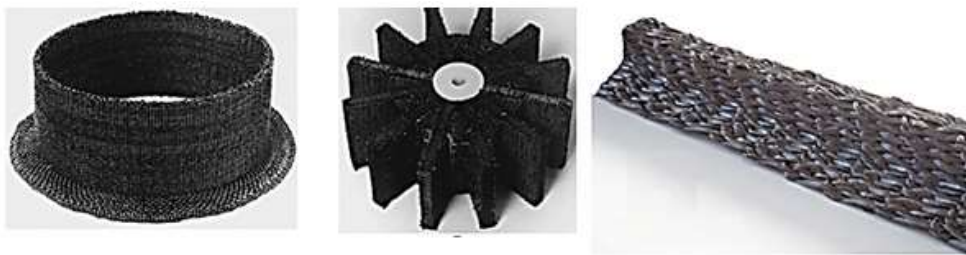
Примеры трёхмерных преформ: корпус, крыльчатка, элемент конструкции
